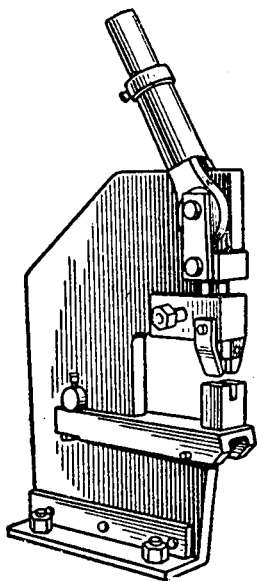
Ручной рычажный пресс для пробивания отверстий
